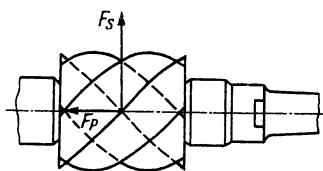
Kräfte am schrägverzahnten Walzfräser
